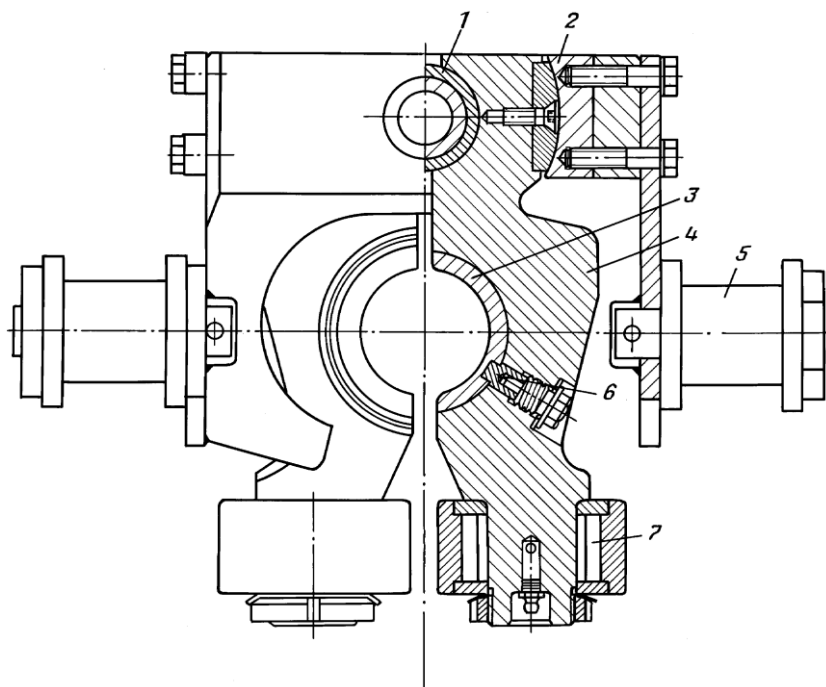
Поперечное сечение узла плашек, захватывающих трубу:
